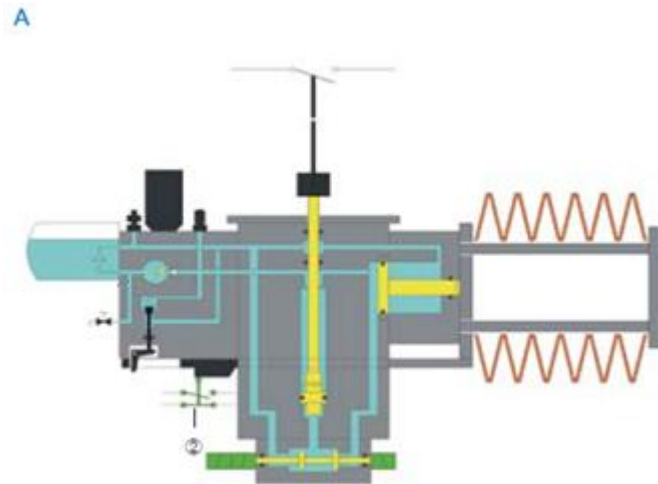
Estado de posición abierta con el resorte sin tensar
